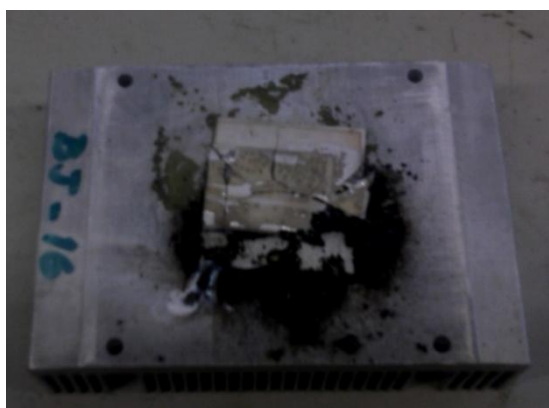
Componentes após tentativa de soldadura. É possível ver que a placa de circuitos ficou completamente inutilizada. Na face da placa de circuitos é visível que a metalização fundiu e que a reacção foi incompleta, devido à presença de material de brasagem não fundido.
